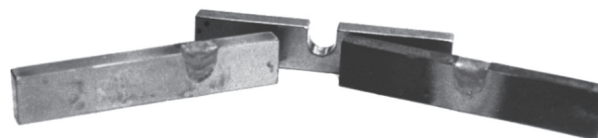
Внешний вид образца с запаянной разделкой дуговой пайкой в вакууме с подачей ПКП
